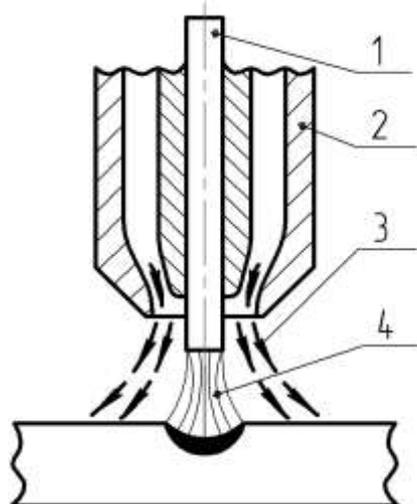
Схема процесса сварки в защитной среде защитного газа:
